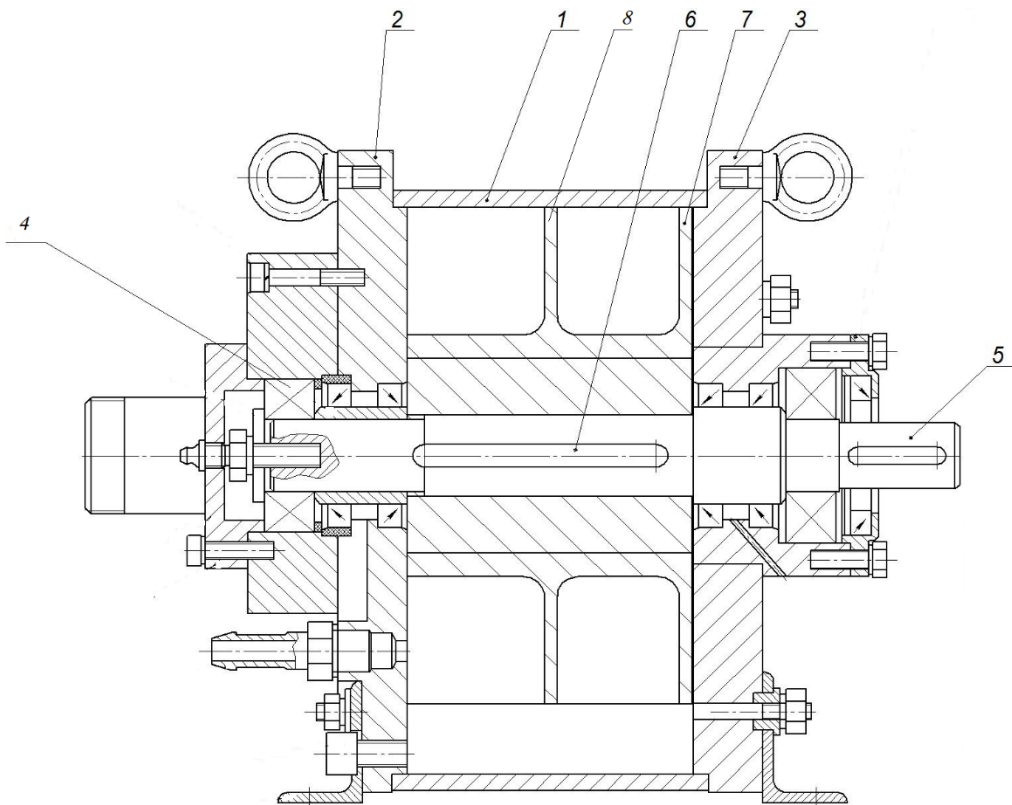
Водокільцевий вакуумний насос ВВН-70 (модернізований): 1 – корпус; 2 – лобовина ліва; 3 – лобовина права; 4 – підшипник; 5 – вал; 6 – шпонка; 7 – колесо; 8 – перегородка
